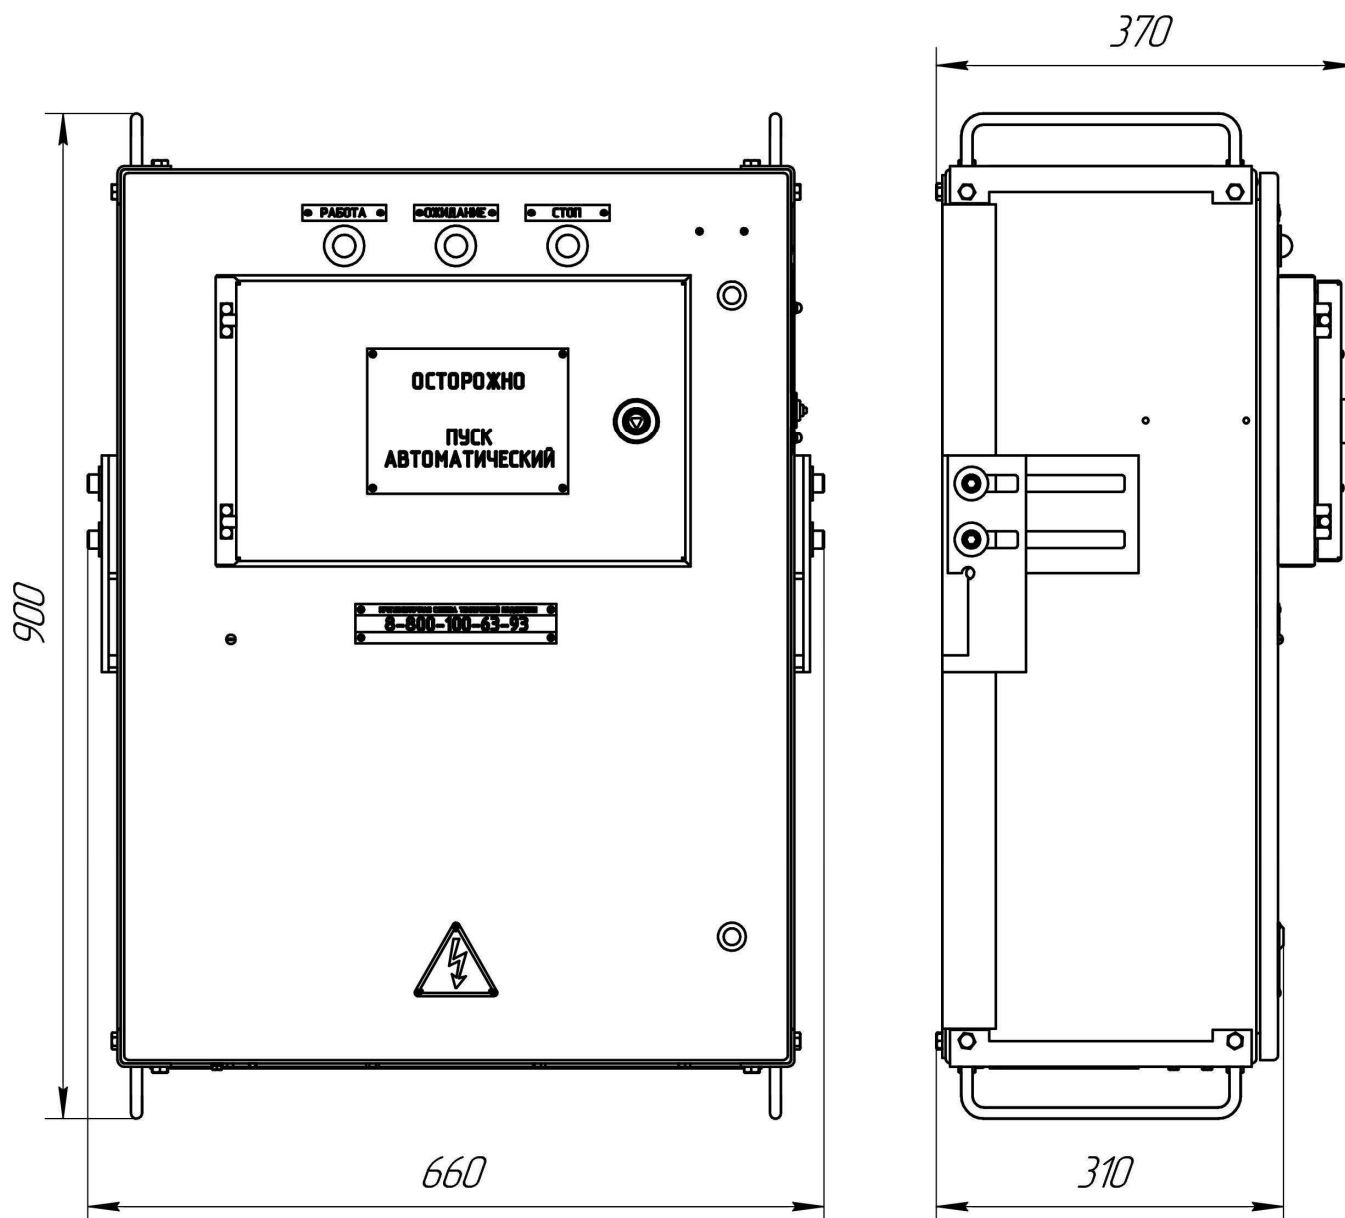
Внешний вид, габаритные и установочные размеры станции управления
